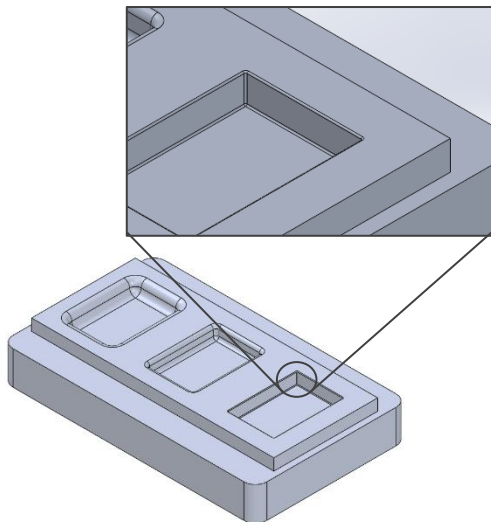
Desenho CAD molde com razão de estiramento de 1,33 – 1,5
